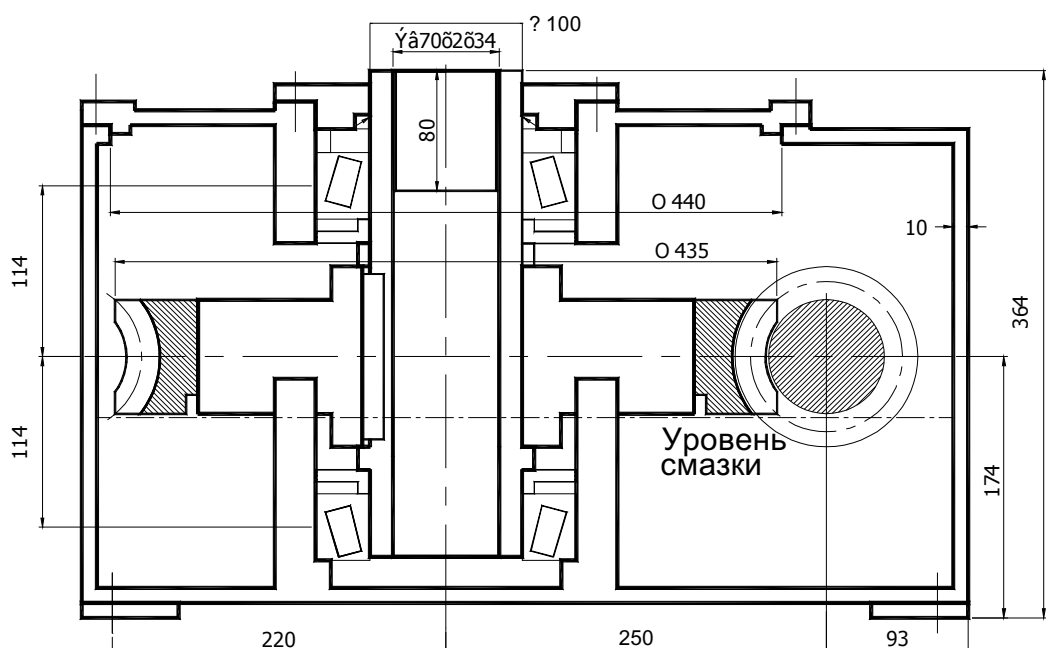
Компоновка редуктора с горизонтальными валами и верхним расположением червяка
